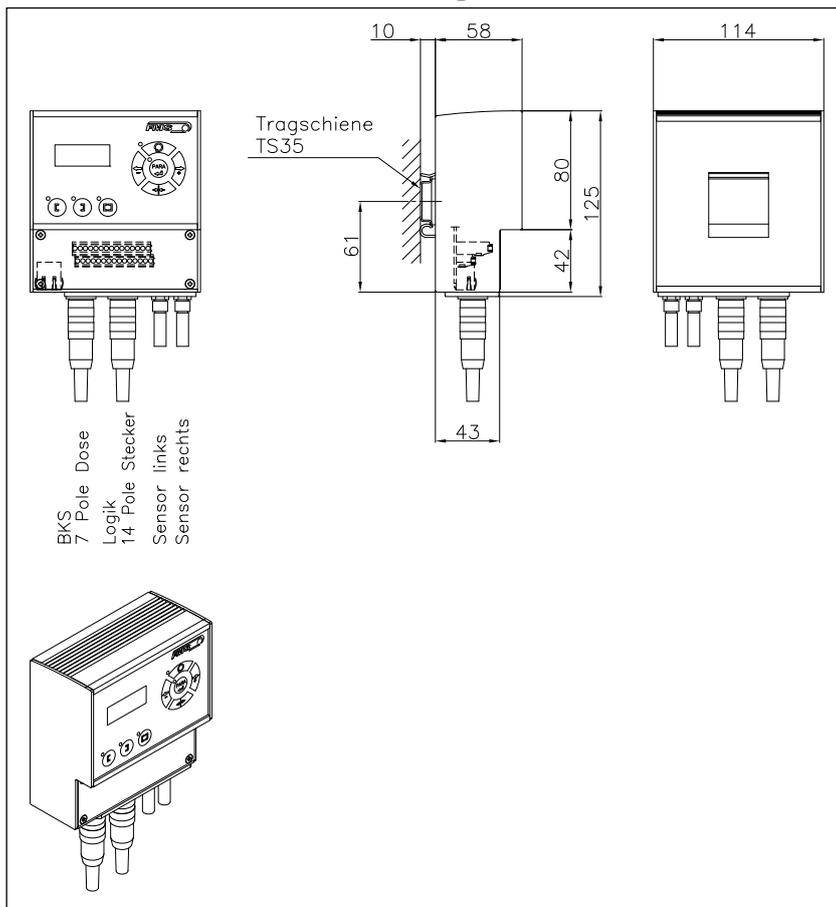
Mechanische Abmessungen BKS309.R.C für DIN-Schienenmontage mit Stecker
